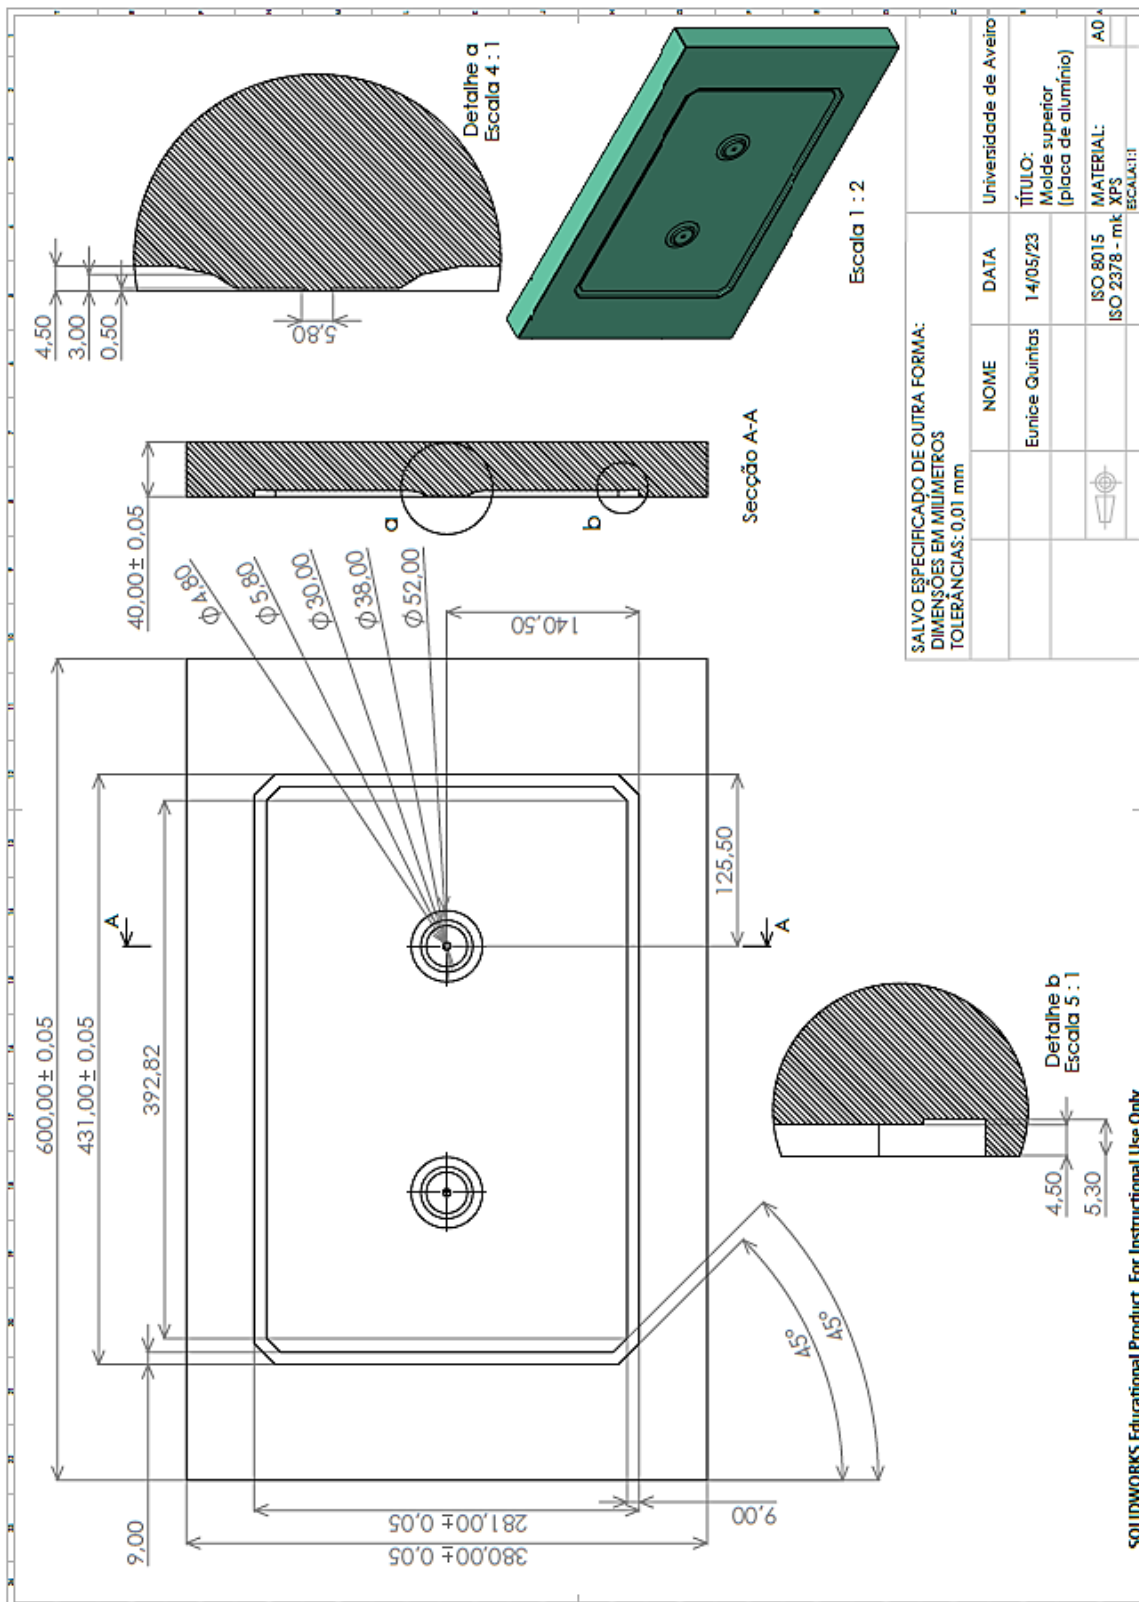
Desenho técnico do molde superior de XPS para a placa de alumínio.
